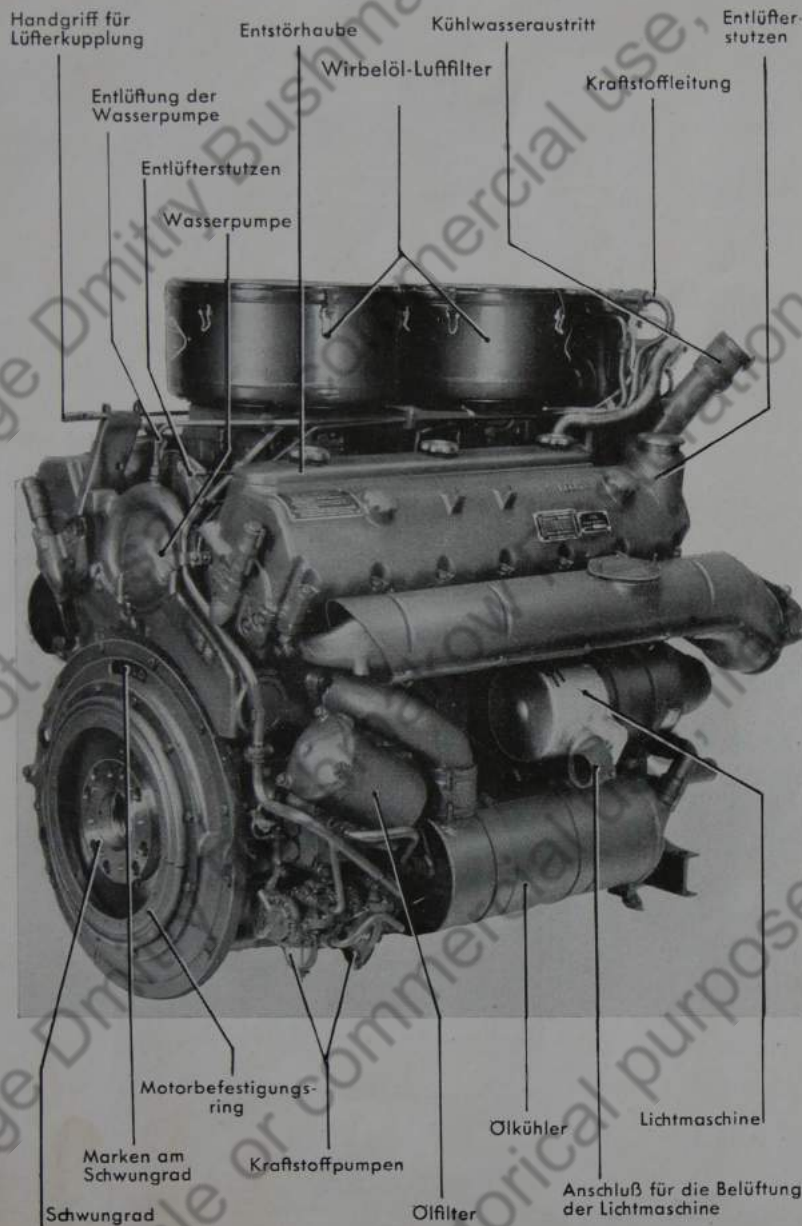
Motor, Lichtmaschinenseite (Wirbelöl-Luftfilter)
